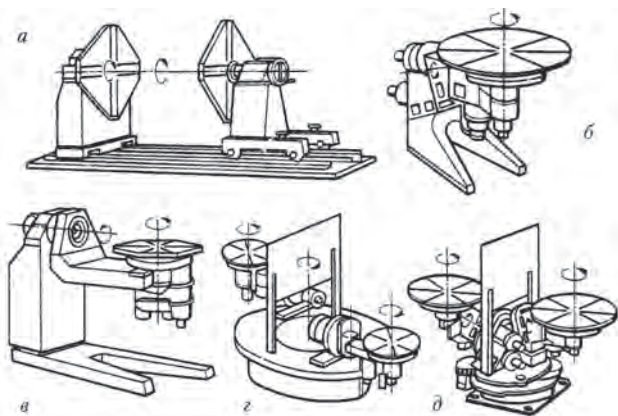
Манипуляторы изделия с программным управлением для оснащения робототехнологического комплекса для дуговой сварки: а – сварочные горизонтальные двухстоечные вращатели - 402М и М150530; б, в – сварочные универсальные вращатели - М150400 и М150500; г, д – сварочные универсальные двухпозиционные вращатели - М150310 и М150410
